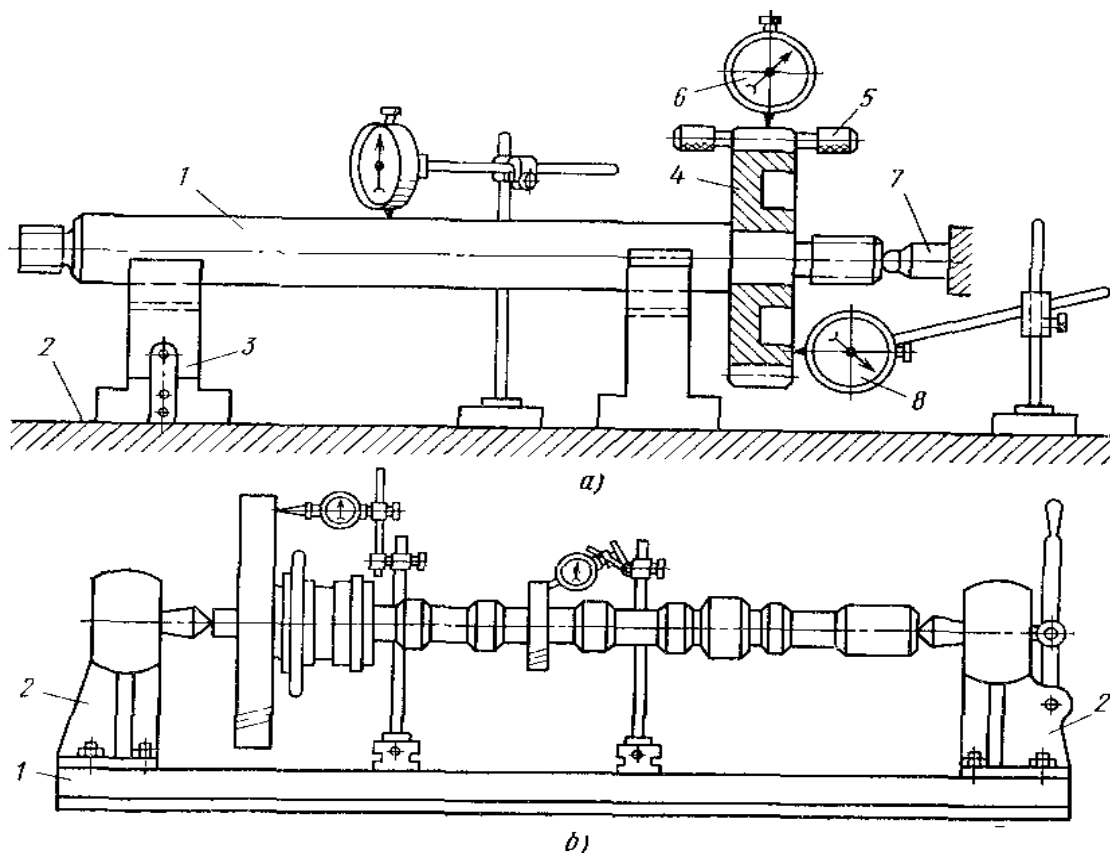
Контроль на биение узла зубчатое колесо — вал:
